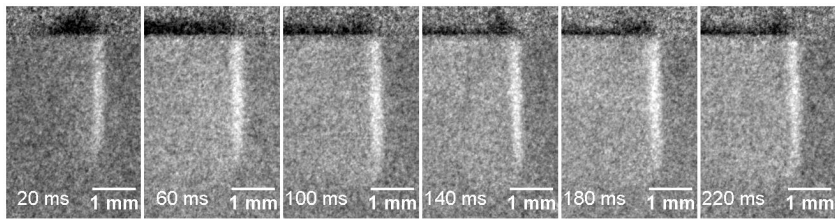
Kapillarausbildung während einer Schweißung in Stahl. Einzelbilder einer Röntgenaufnahme vom Schweißprozess in 16CrMn5, $P = 2,4 \text{ kW}$, $v = 3 \text{ m/min}$, $d_r = 200 \text{ }\mu\text{m}$, Anstellwinkel 0° , Einschweißung. Framerate X-Ray = 1000 Hz.
